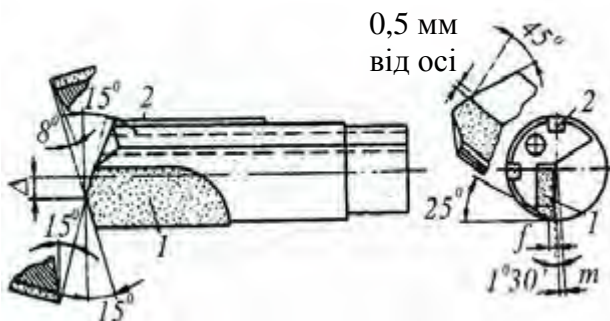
Свердло рушничне з припаяною пластинкою з твердого сплаву
